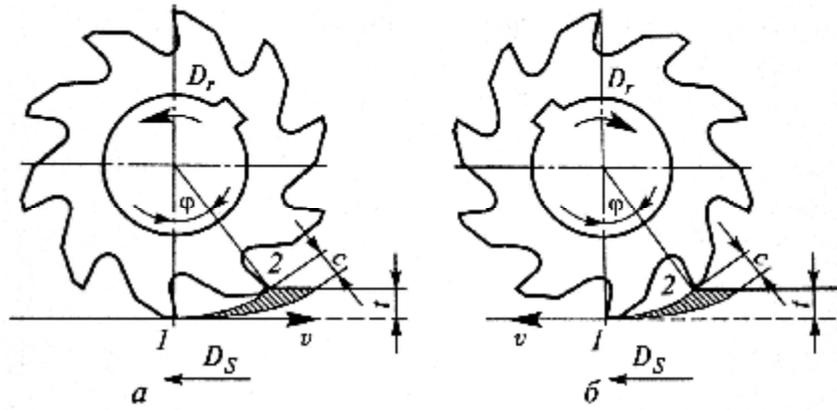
Схемы фрезерования: *а* – встречного; *б* – попутного
